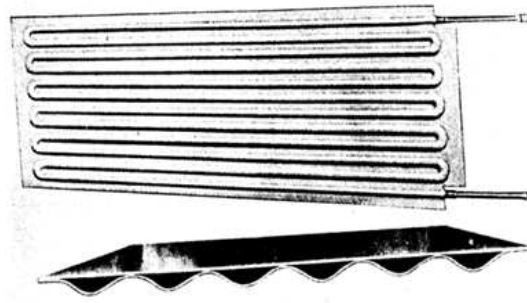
Evaporador serpentín estándar de placas³⁶
